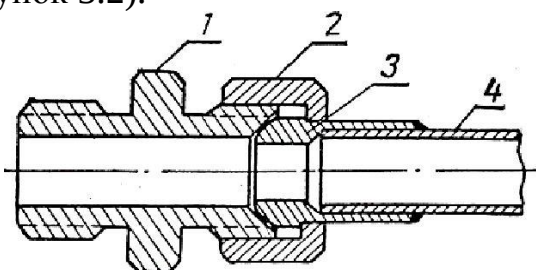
Присоединительное устройство трубопроводов:
